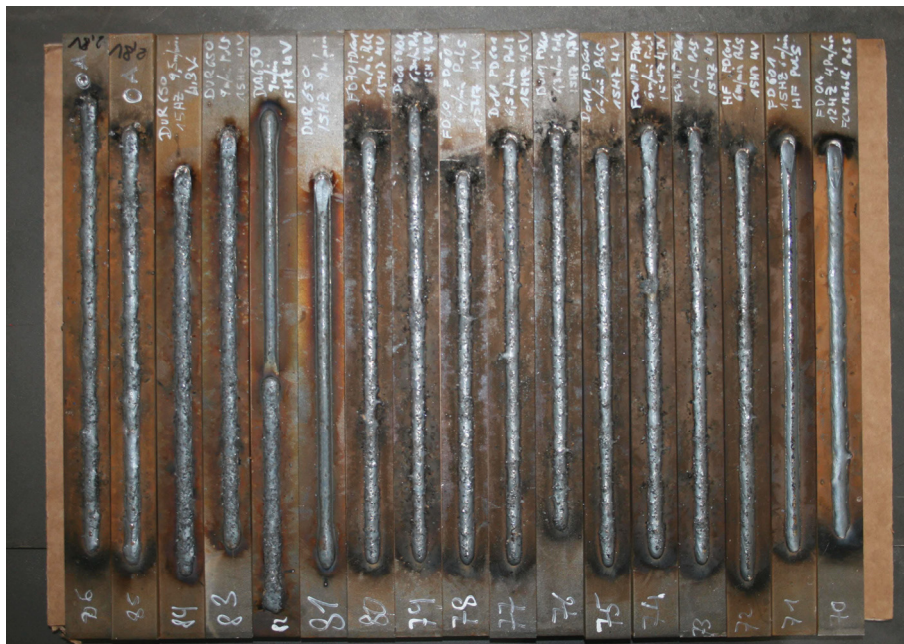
Probeplatte mit Versuchsschweißungen
